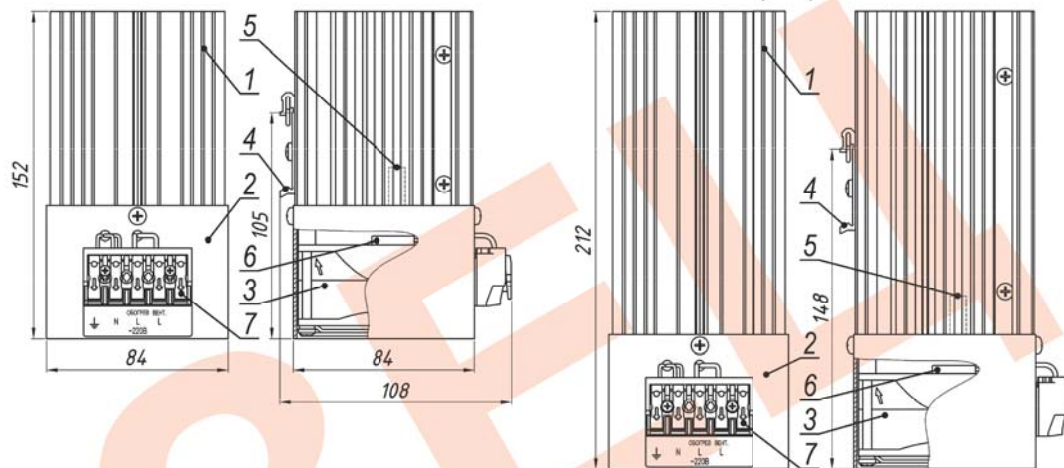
Устройство и габаритные размеры ОТШ-100 (-160, -200, -300)
